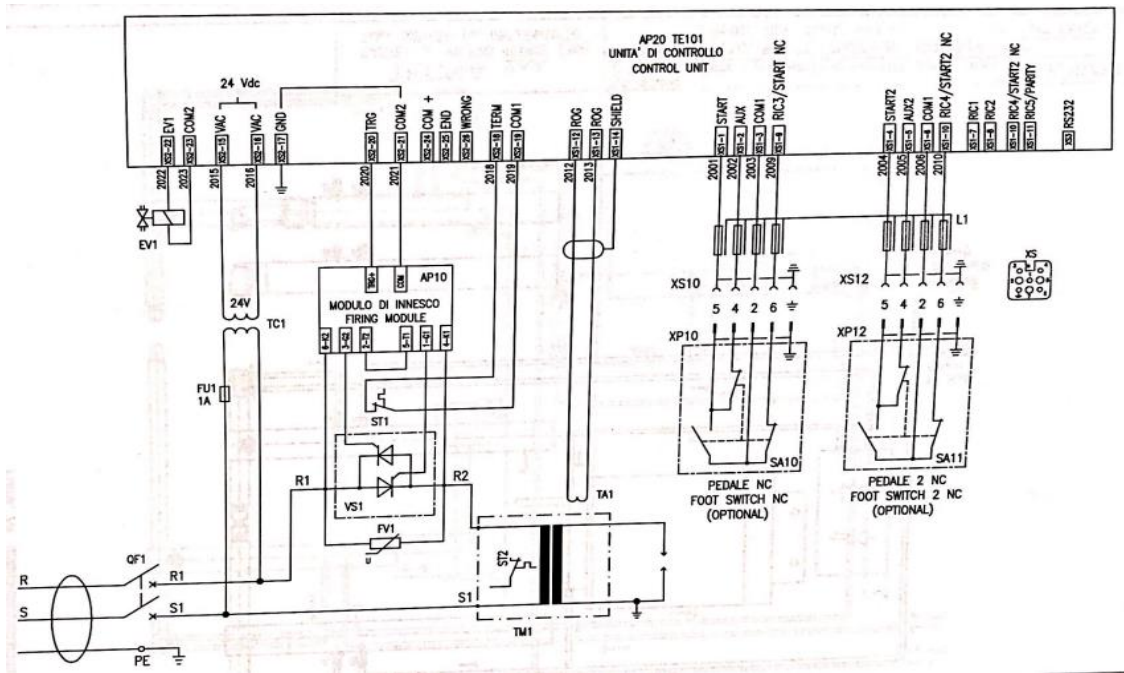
Esquema de Cableado Art. 4045-49N de la Soldadora de Punta.
